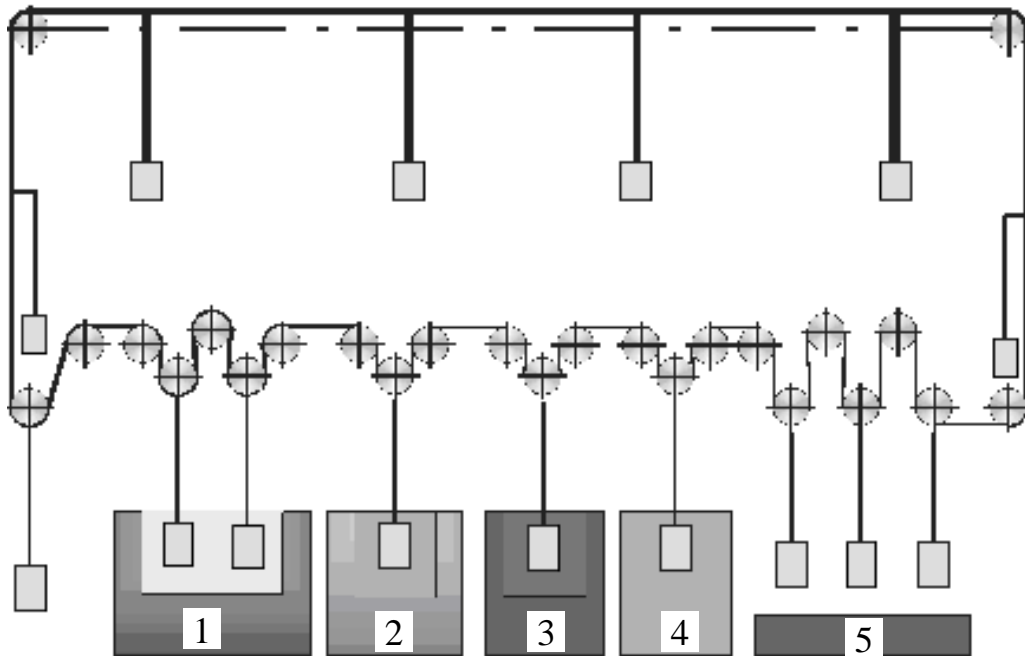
Схема напівавтоматичного гартівного агрегату ТА-22
